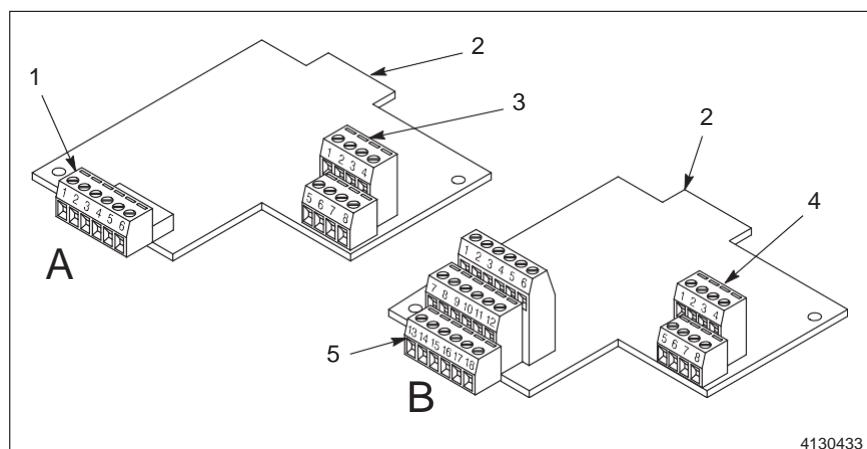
Placas I/O Padrão (A) e Aprimorada (B)
